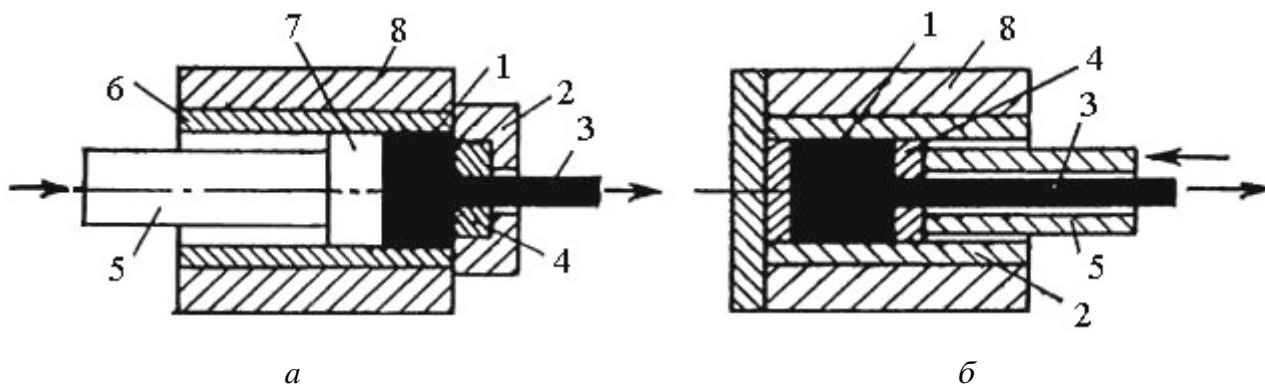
Схема процесса прессования: а – прямое прессование; б – обратное прессование:
